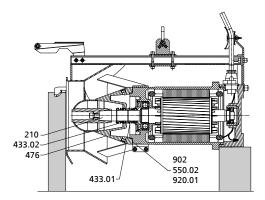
Desmontaje del cierre mecánico en Amaline 300 con motor 86
